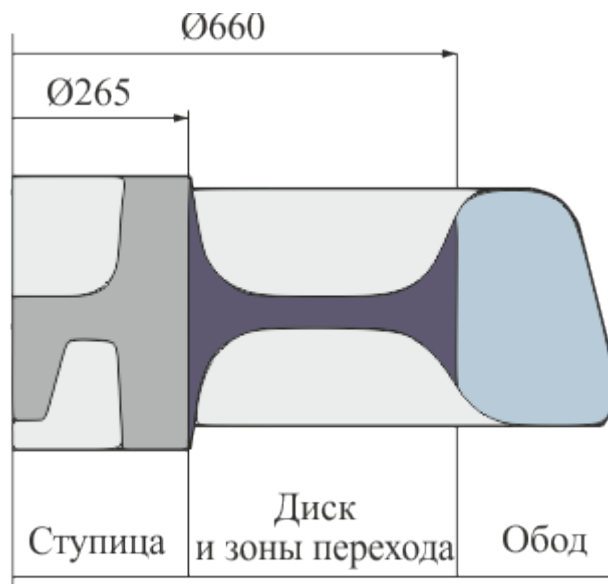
Разделение поковки колеса на конструктивные элементы
